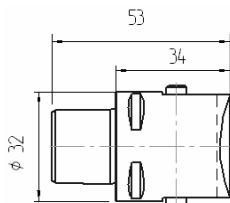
Корпус C3-391.68A-3-032 034 B ( $Z_n = 2$ )
